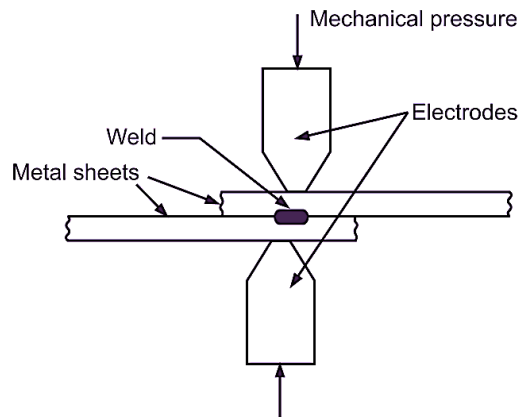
Esquema de proceso de soldadura de punto y sus variables. [14]
